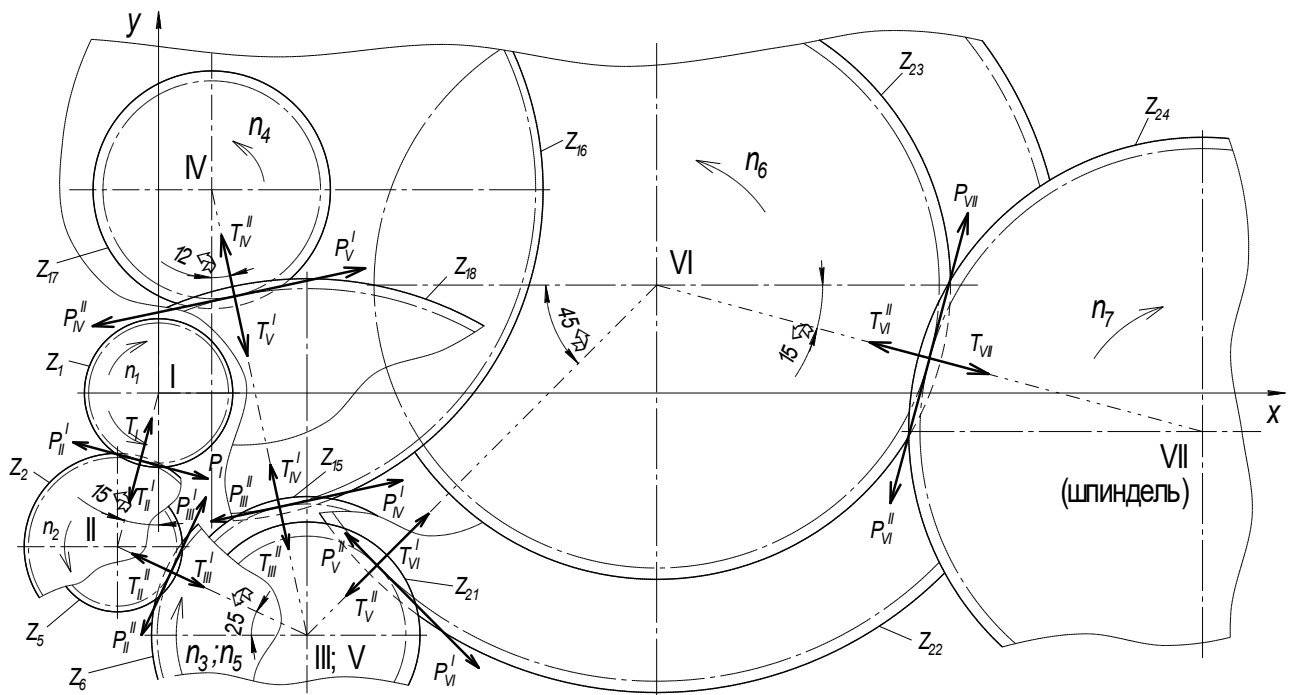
Схема згортки валів коробки швидкостей
